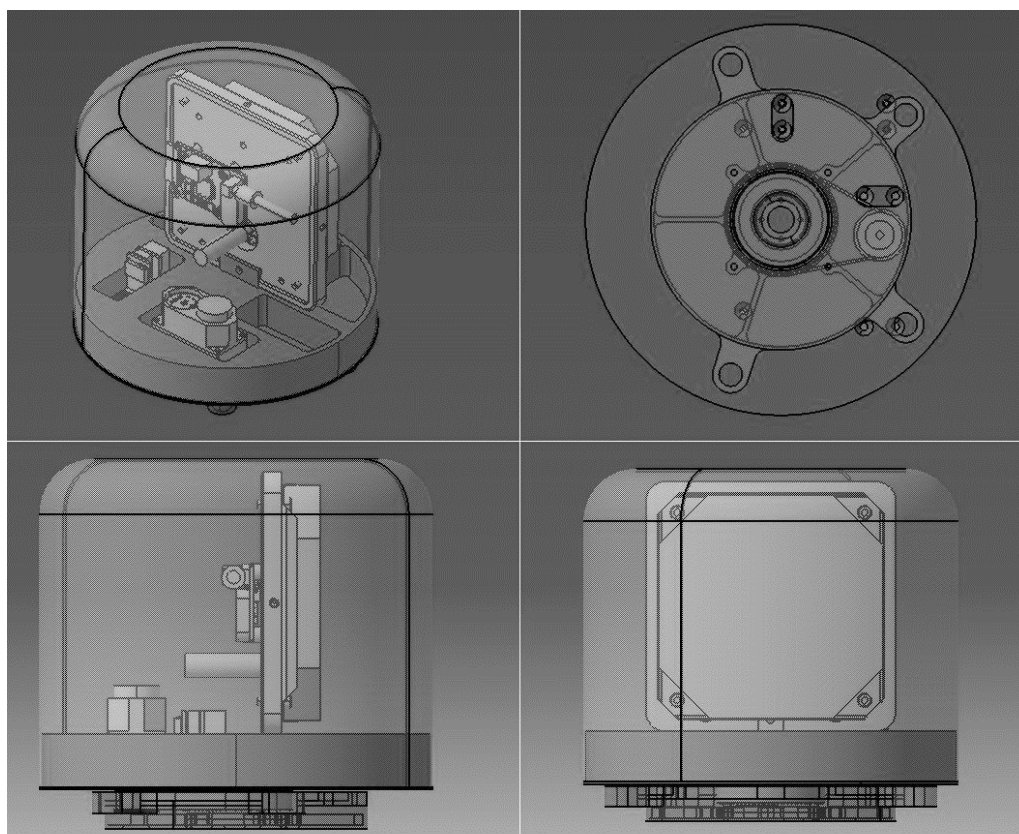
Опорно-поворотное устройство для борта БПЛА
